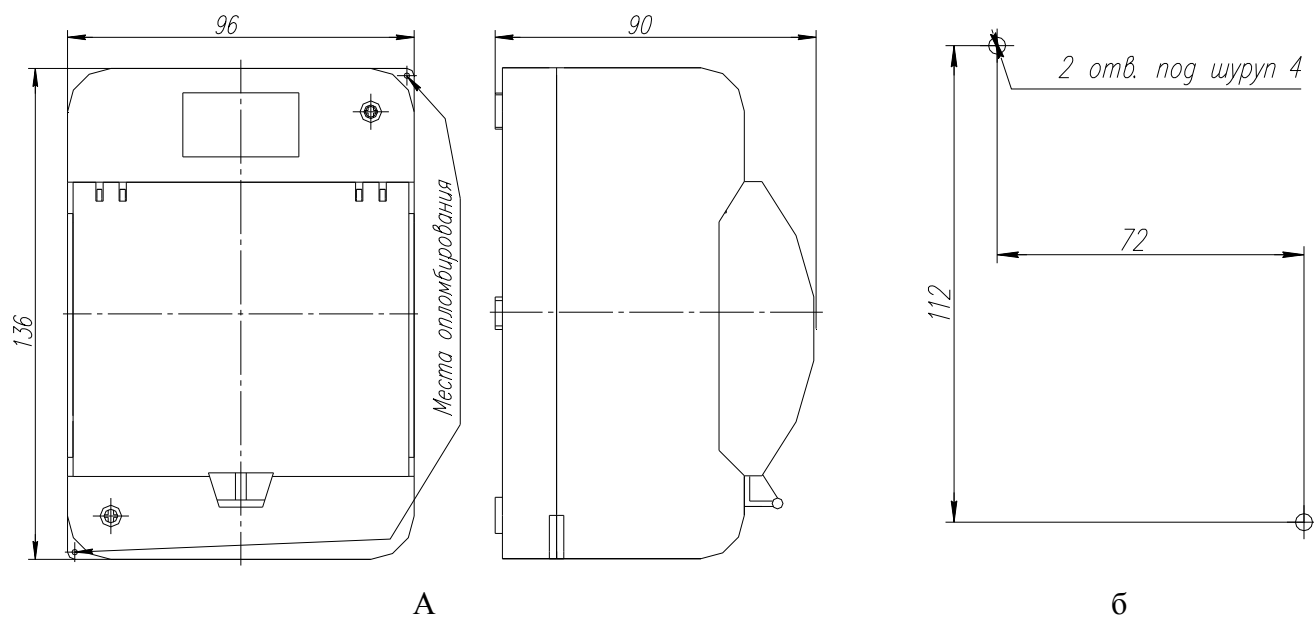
Внешний вид и габаритные размеры(а), установочные размеры (б) блоков БКА-220, БКА-12, БКА-24, размеры в мм.
